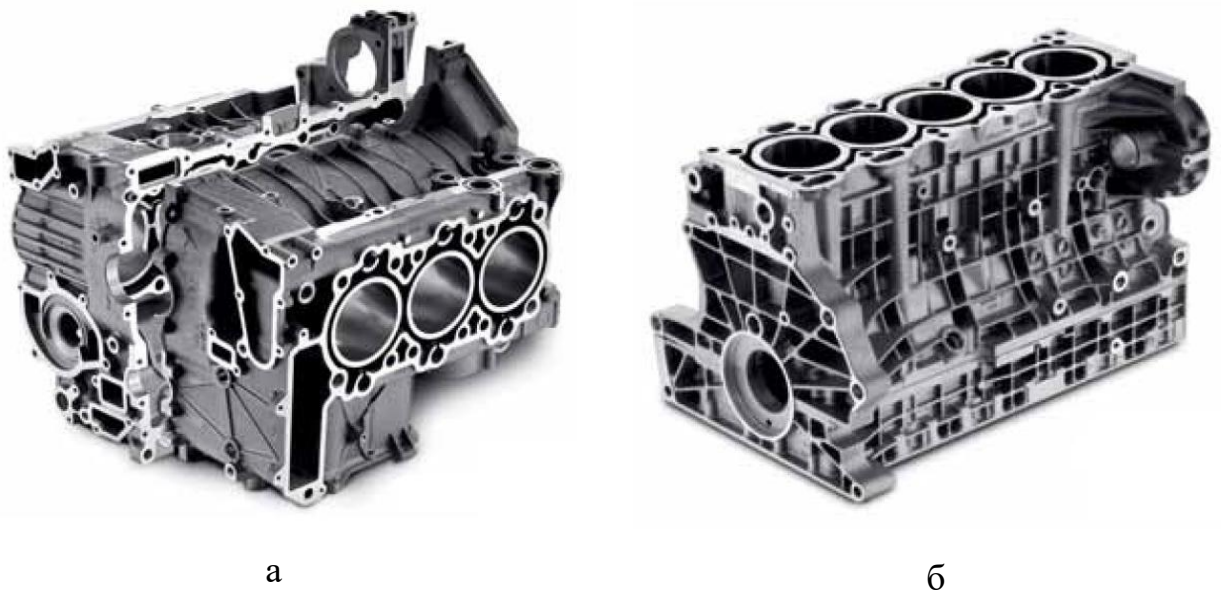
Блоки цилиндров конструкции типа «Open-Deck» [21]
